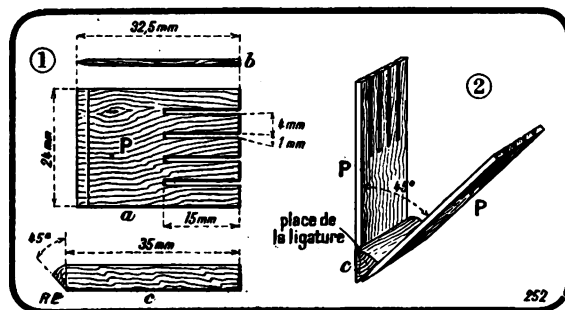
et 2. — Construction et assemblage des pales de bobines.
